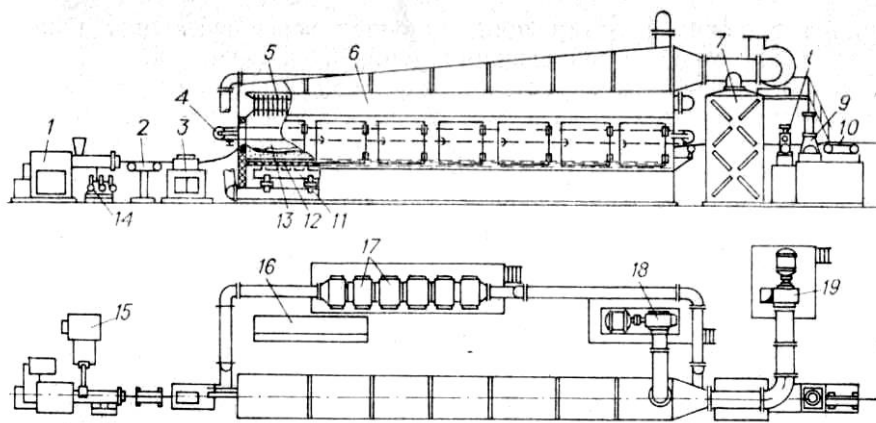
Поточкова лінія для виготовлення профільних виробів з вулканізацією в псевдозрідженому шарі: 1 - черв'ячна машина; 2 - проміжний транспортер, 3 - установка для антиадгезійної обробки заготовки; 4 - заправний пристрій; 5 - реєстр для підігріву повітря; 6 - вулканізатор; 7 - установка для очищення і охолодження готових виробів; 8 - простягаючий пристрій; 9 - ріжуча машина; 10 - приймальний транспортер; 11 - колектор для подачі повітря; 12 - пориста решітка; 13 - ванна вулканізатора; 14 - вакуумна установка; 15 - живильник для подачі гумової суміші в черв'ячний екструдер; 16 - пульт управління; 17 - батарея електрокалориферів; 18 - газодувки; 19 - вентилятор.
